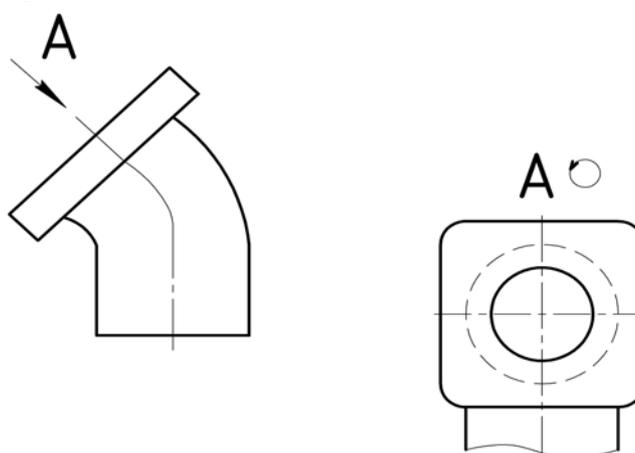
Обозначение дополнительного вида (вид повернут)
